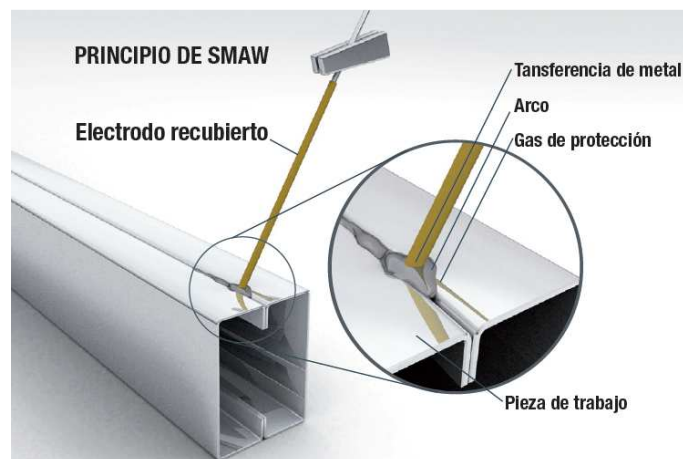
Esquema de aplicación de soldadura SMAW
